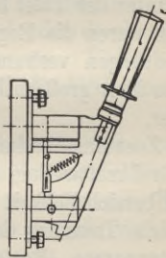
Ein Hebelschalter mit Messerkontakt u. Funkenabreißer.
